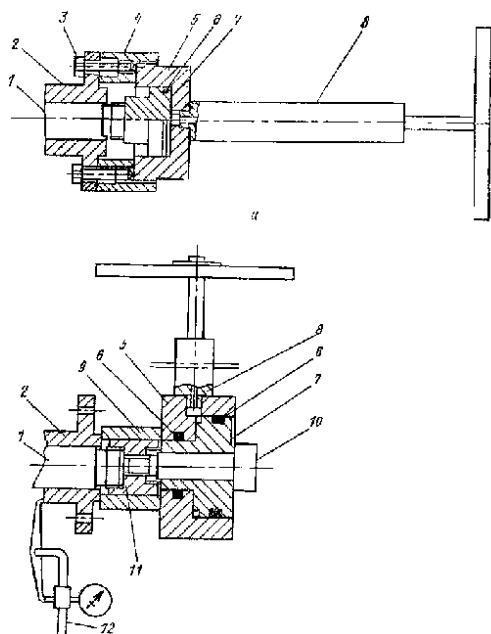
Приспособления для снятия (а) и напрессовки (б) полумуфт на вал центробежного компрессора и мультипликатора
